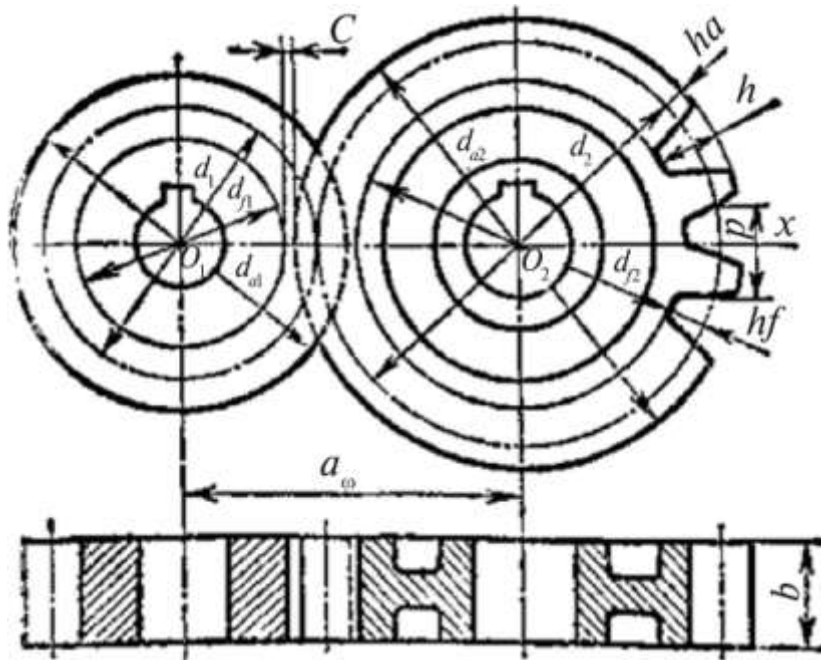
Геометрические соотношения прямозубой цилиндрической передачи
